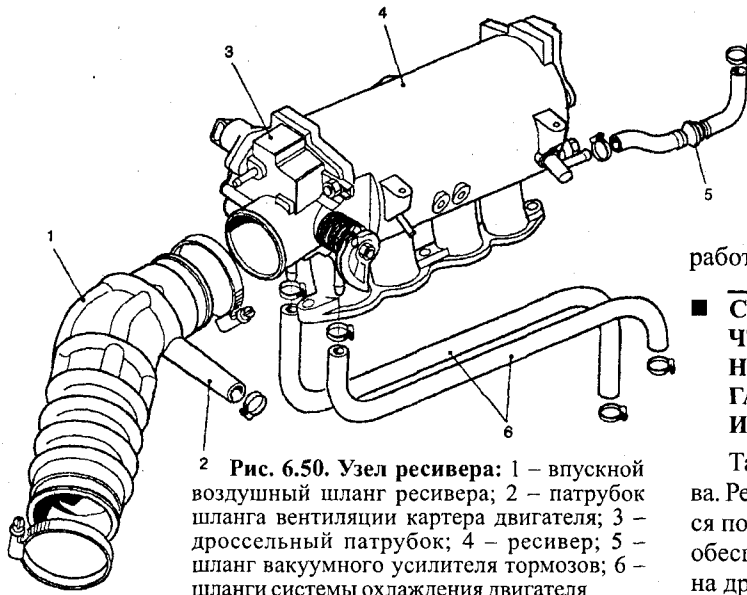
Узел ресивера: 1 – впускной воздушный шланг ресивера; 2 – патрубок шланга вентиляции картера двигателя; 3 – дроссельный патрубок; 4 – ресивер; 5 – шланг вакуумного усилителя тормозов; 6 – шланги системы охлаждения двигателя
